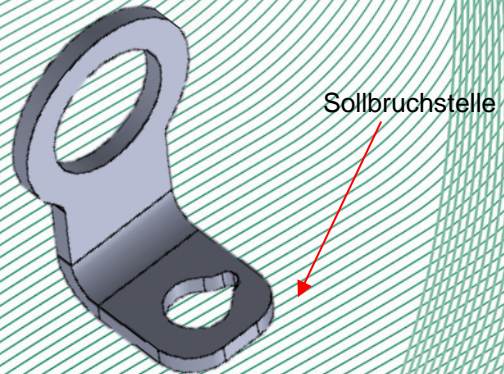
Anschlagpunkt, Typ: TS-Lasche
